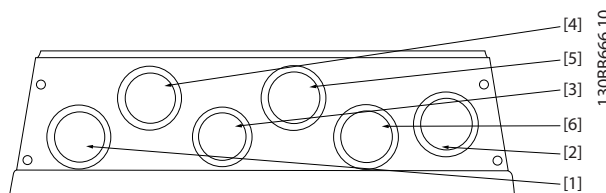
A5- IP55 gängade kabelförskruvningshål
